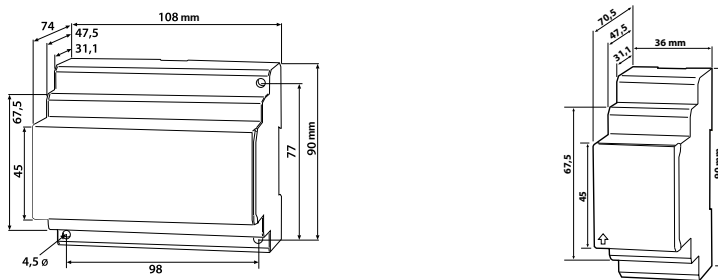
Bemaßung der Gehäuse X460 und X420
